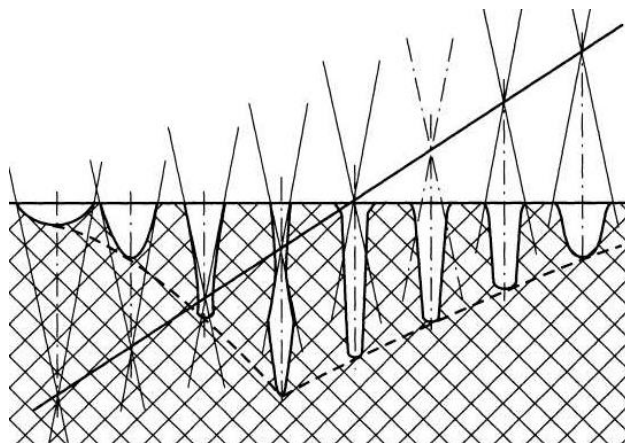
Профили отверстий при различных положениях фокуса лазерного луча относительно поверхности обрабатываемой детали
